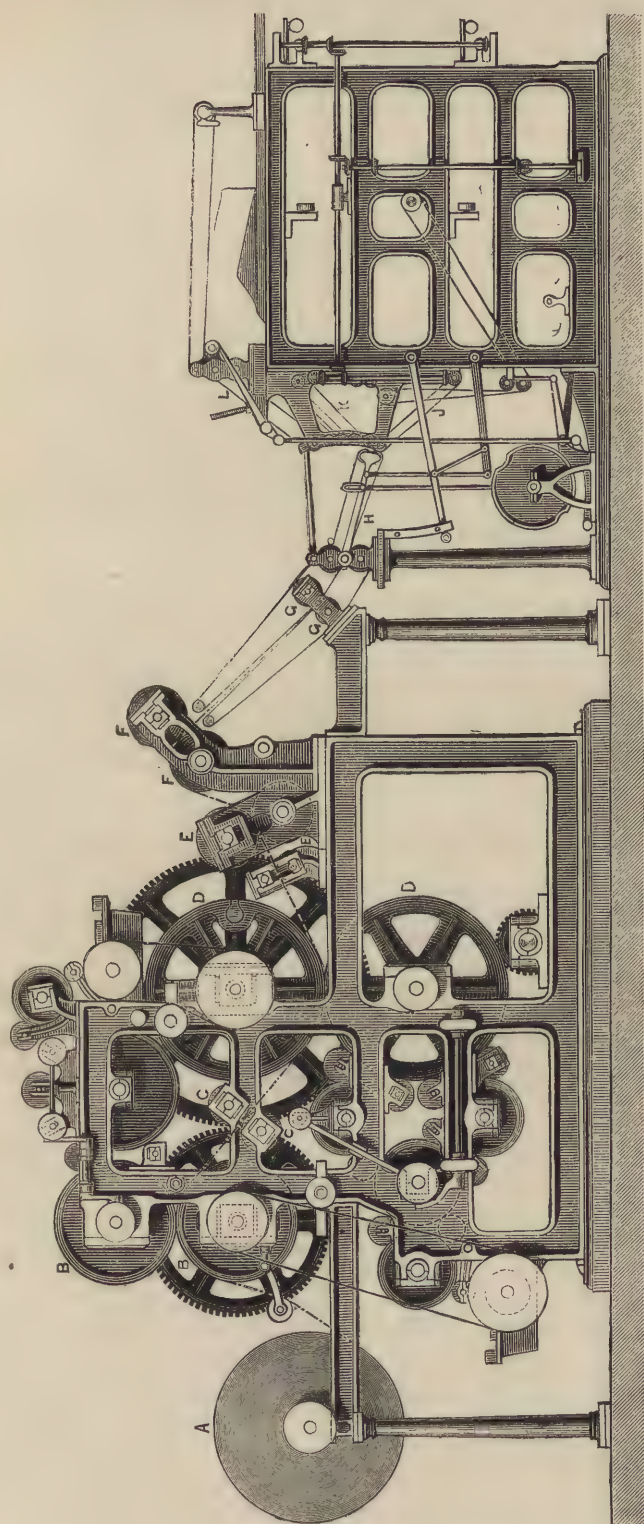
MACHINE CYLINDRIQUE A PAPIER CONTINU « INGRAM »
